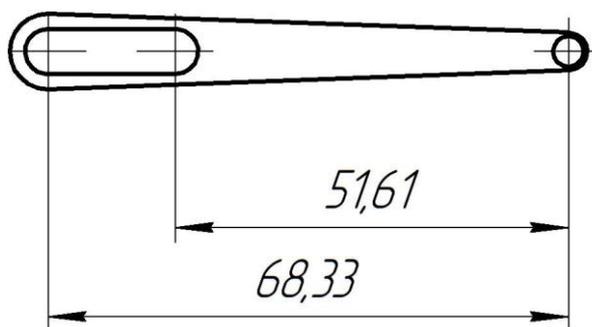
Эскиз толкателя с рассчитанными размерами.
